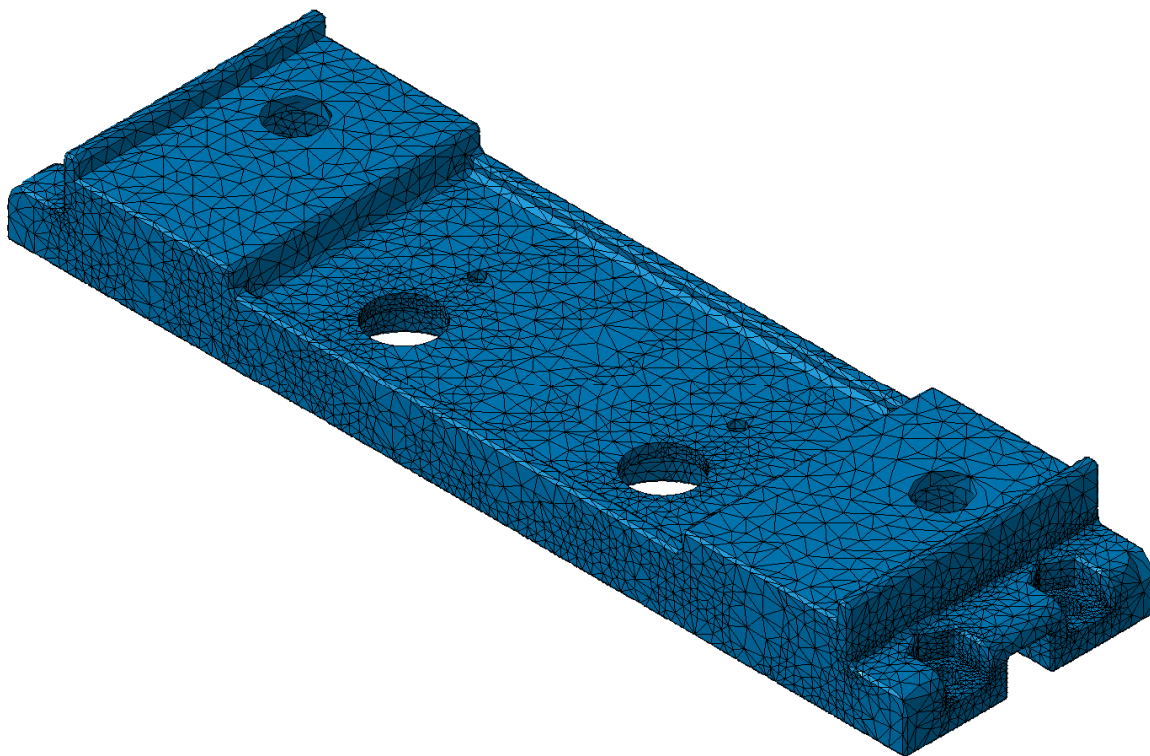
3D model – 5. varianta držáku – horní pohled
